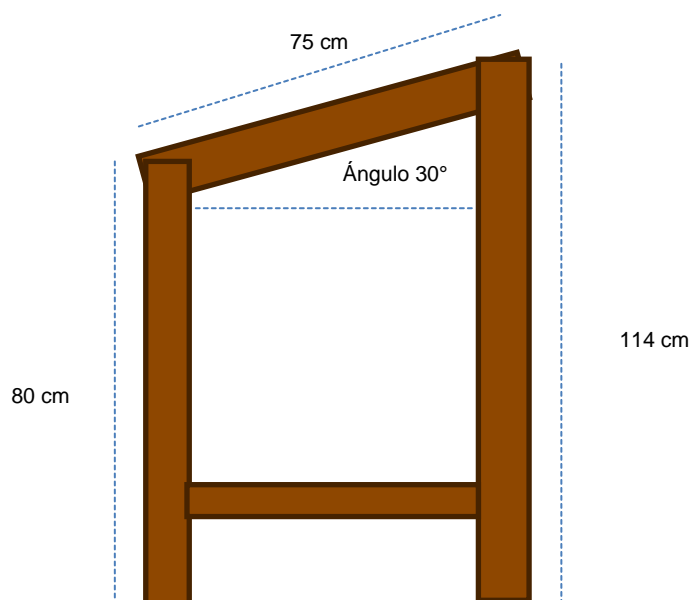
Dimensiones de la base de madera para sujetar el panel
